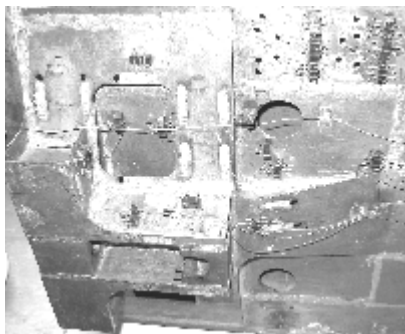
Элементы из листового металла, соединенные сваркой
